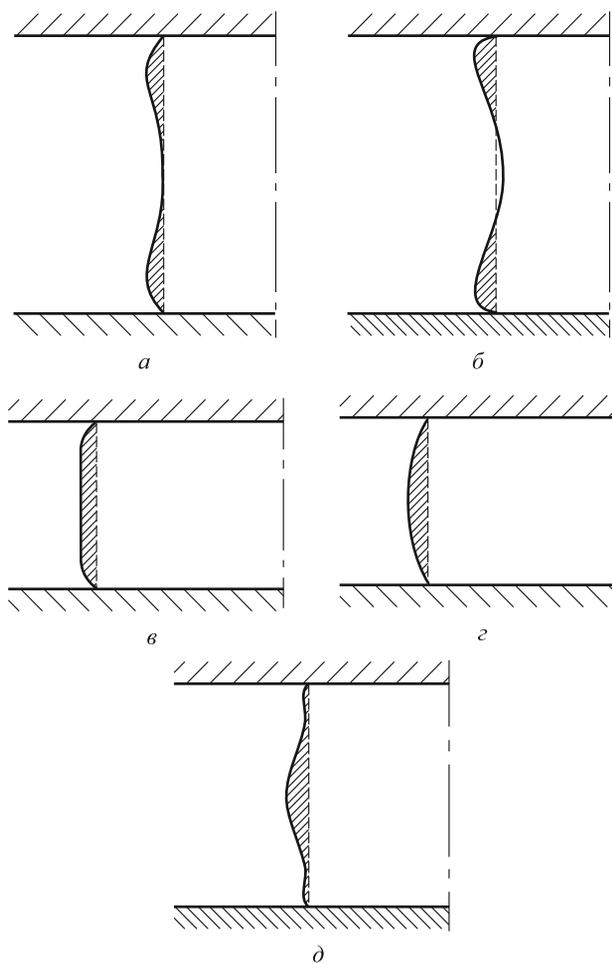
Пример одинакового объема бочкообразности (заштрихован) у заготовок с различными формами бочек:
